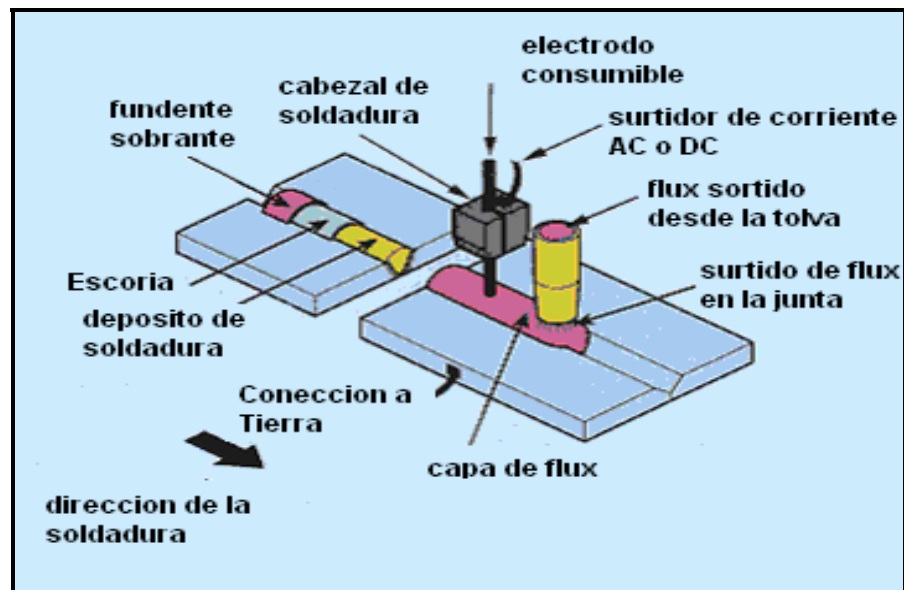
Proceso de soldadura por el método de arco sumergido.
